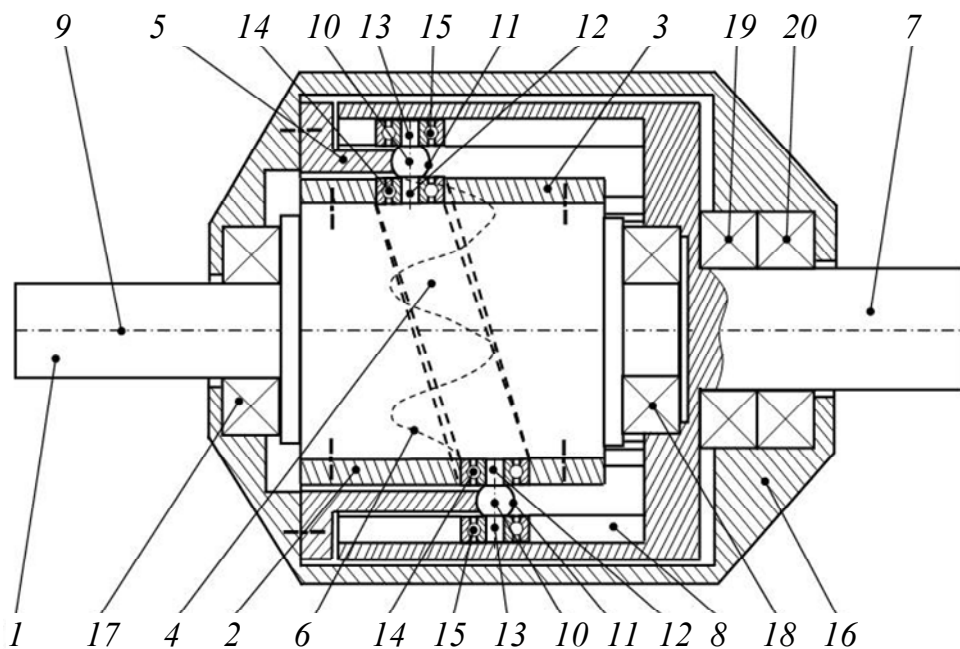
Схема ППТК цилиндрического типа с качением во всех кинематических парах (патент Республики Беларусь 6376)
